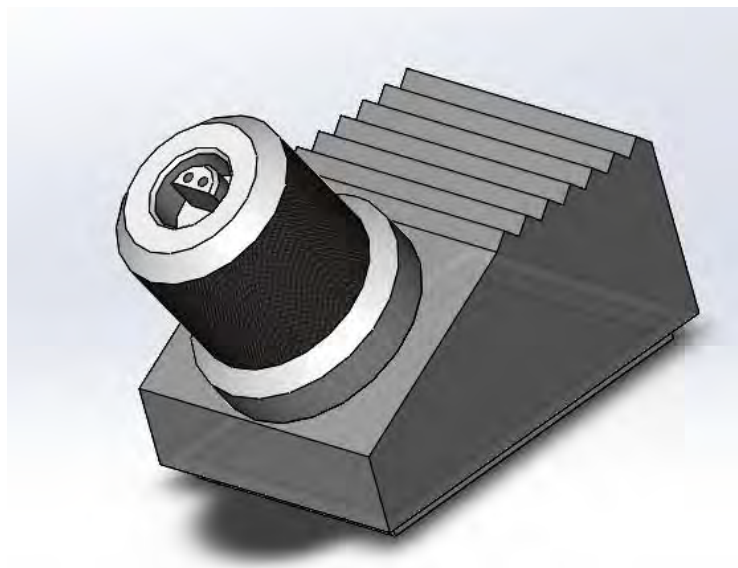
Зовнішній вигляд корпусу давача та призми
